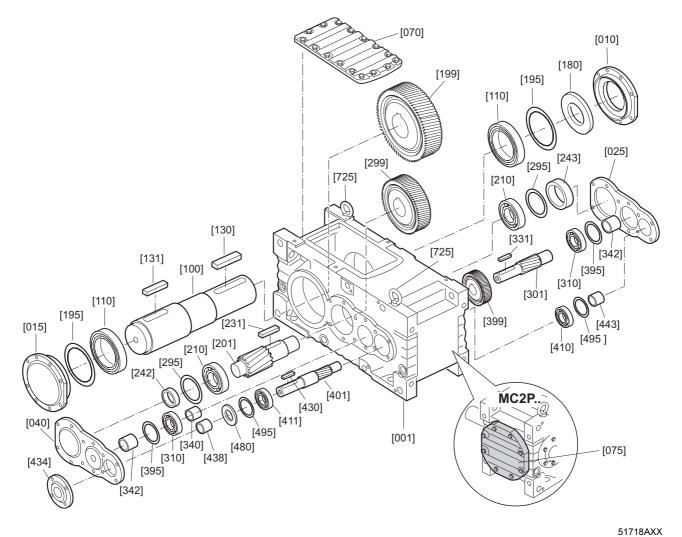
Базовая конструкция индустриального редуктора МС..Р..
